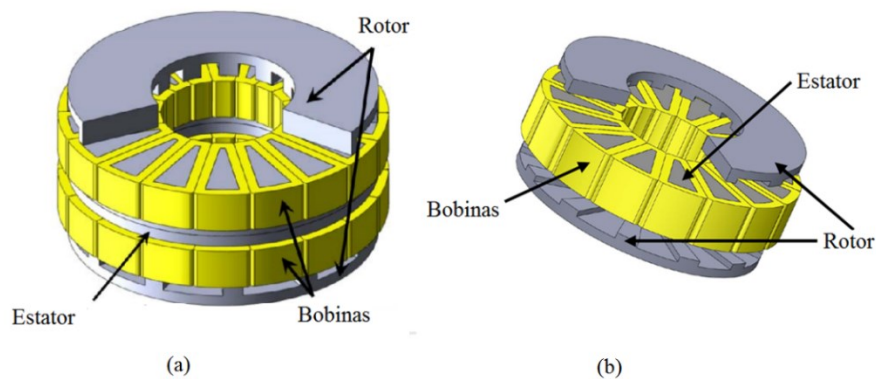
Máquina de relutância chaveada de fluxo axial, modular e caminhos reduzidos de fluxo magnético no rotor 12s/10p: (a) Vista da máquina, (b) Vista explodida da máquina.
